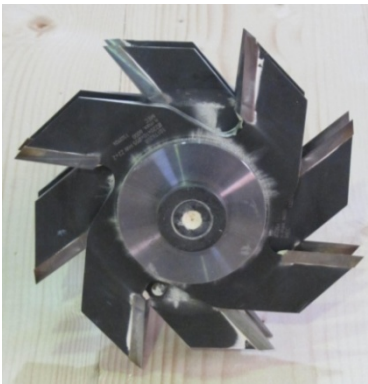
Fräs Werkzeug für das neu entwickelte Keilzinkenprofil 40-10-1,4
